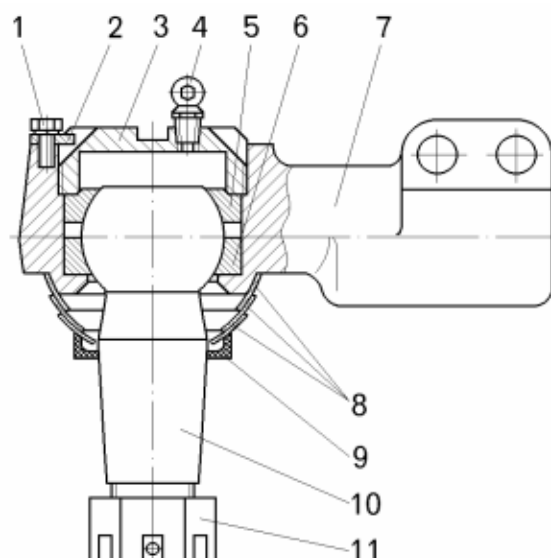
Шарнир гидравлического цилиндра поворота:
